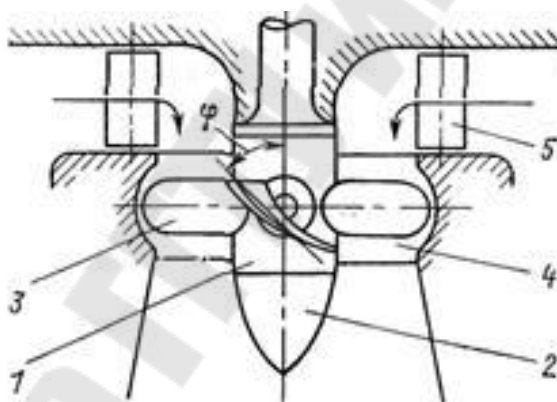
Рабочее колесо поворотно-лопастной турбины: 1 — корпус рабочего колеса; 2 — обтекатель; 3 — лопасти; 4 — камера рабочего колеса; 5 — лопатки направляющего аппарата.
